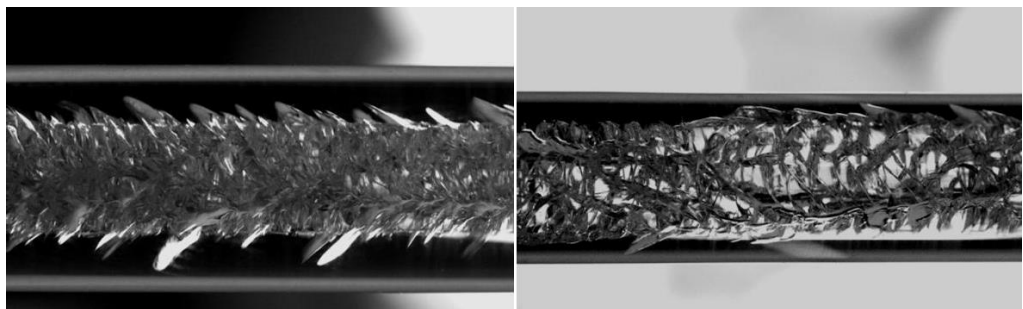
Разрушения заготовки силового стержня [135]
